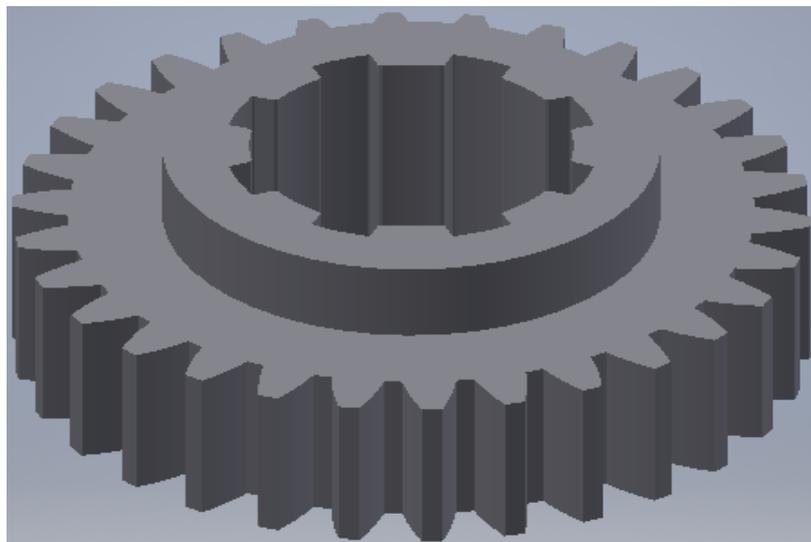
Трехмерная модель шестерни коробки передач токарного станка
